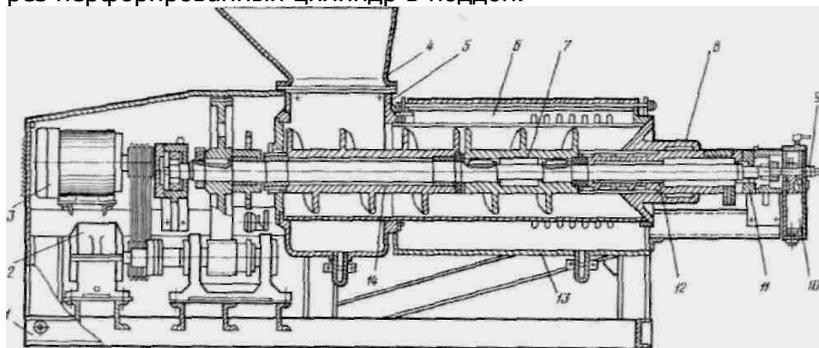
Пресс ВПО-30А: а - разрез общего вида (1 - рама; 2 - редуктор; 3 - электродвигатель; 4 - бункер; 5 - корпус; 6 - цилиндр; 7 - прессующий шнек; 8 - конус; 9- гидроцилиндр (блок управления); 10 - насос; 11 - опора; 12 - барабан; 13 - поддон; 14 - транспортирующий шнек
